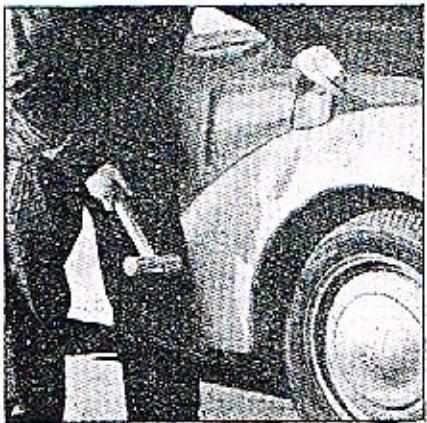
Páka k hrubému vyrovnávání předních částí blatníku
